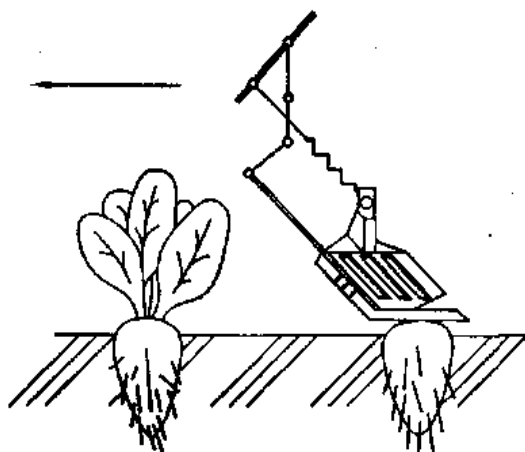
Гичкозрізувальний пристрій, в якому ріжучий елемент виконує поступальний рух
